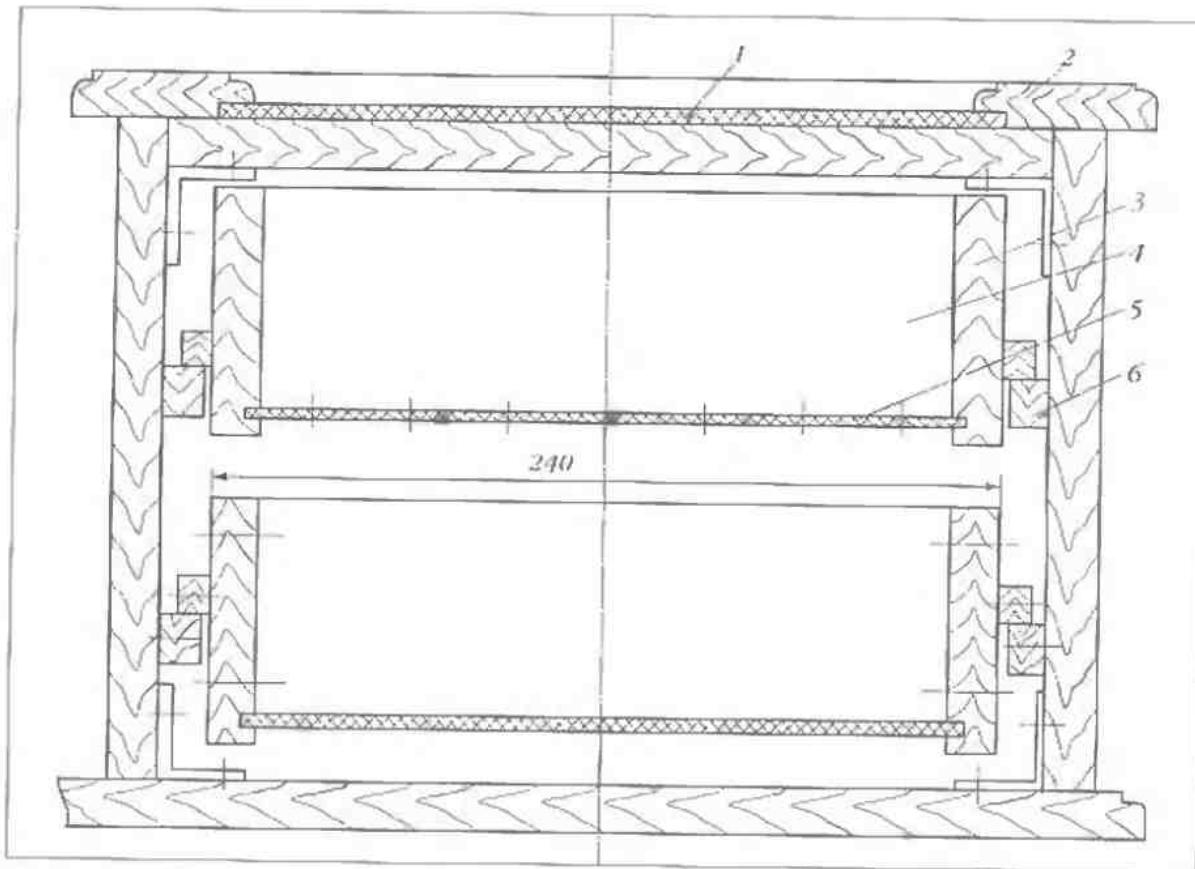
Тумбочка диванчика в разрезе (масштаб 1:2): 1 – акладыш (лист ДВП, оббитый тканью); 2 – верхний крышка тумбочки; 3 – боковина ящика; 4 – задняя стенка ящика; 5 – донце ящика; 6 – направляющая рейка
